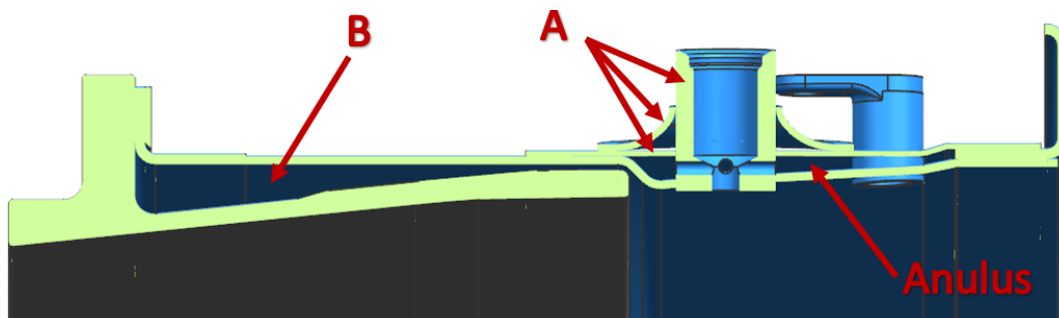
Vista de sección transversal de la unión preliminar del Turbine Bearing Support y el Exhaust Nozzle. A) Arreglo para el sensor de presión P5 y B) Claro entre ambos componentes
